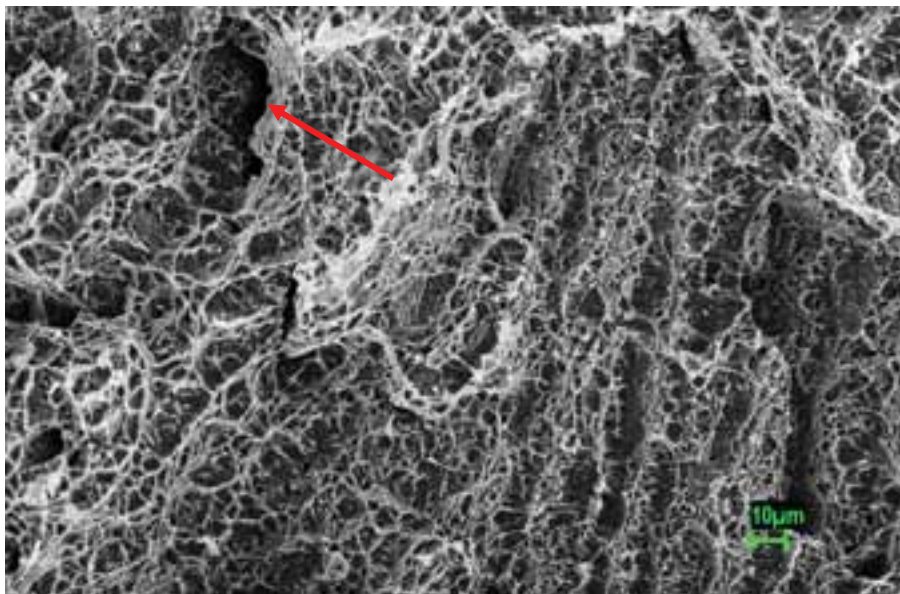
Superfície da fratura do corpo de prova soldado na condição de um reparo
